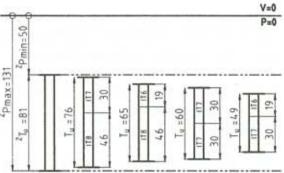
Polohy tolerančních polí - výběr ze soustavy tolerancí a uložení ISO
